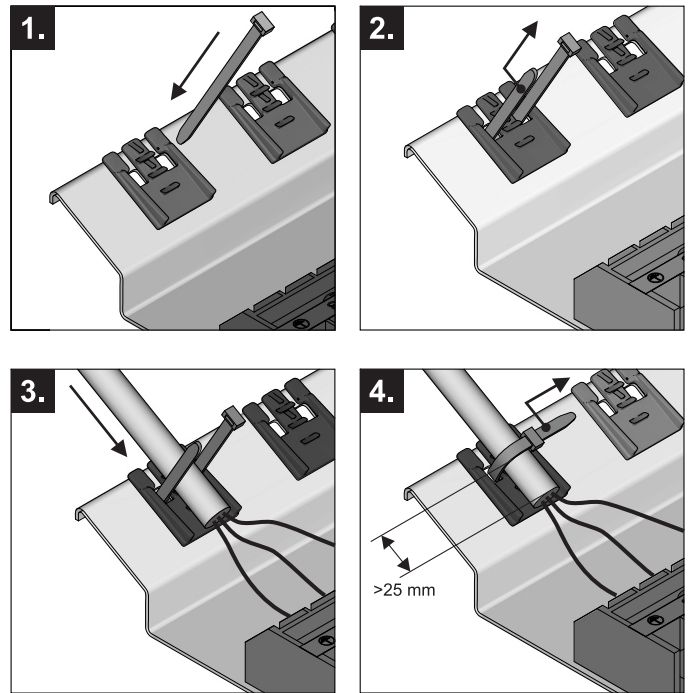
Halteclip einrasten und Kabel mit Kabelbinder festzurren
